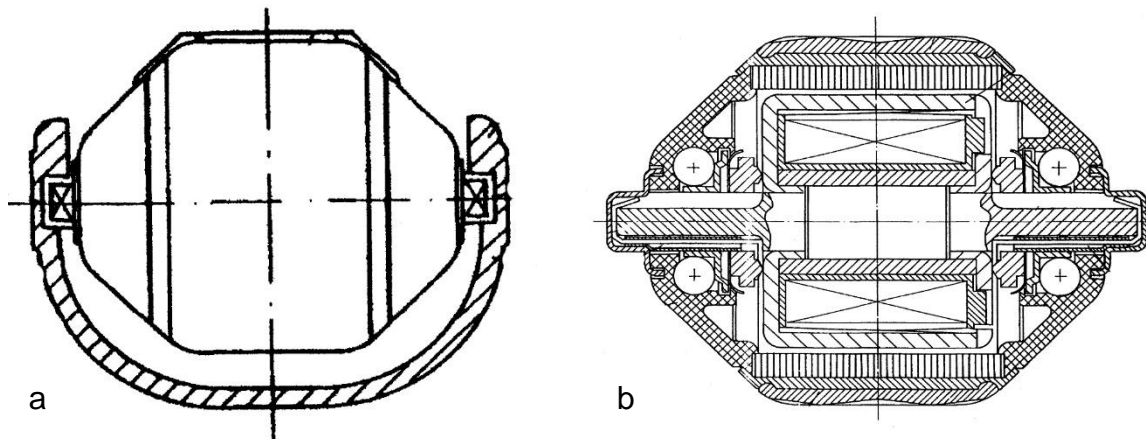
Generator: a) Aufhängung, b) Querschnitt
